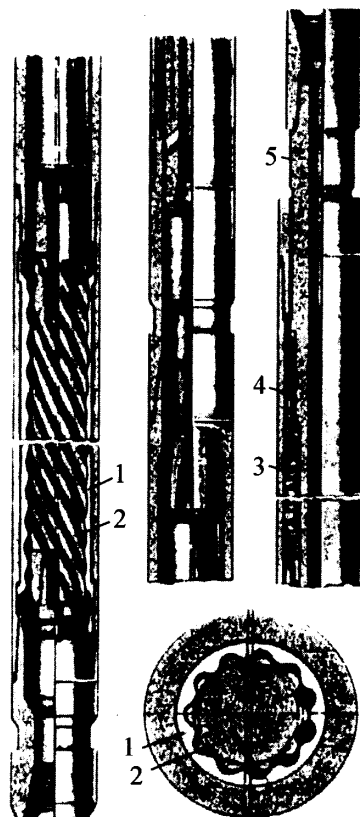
Винтовой забойный двигатель: 1 – статор; 2 – ротор; 3 – упорный подшипник; 4 – радиальный подшипник; 5 – вал шпинделя
